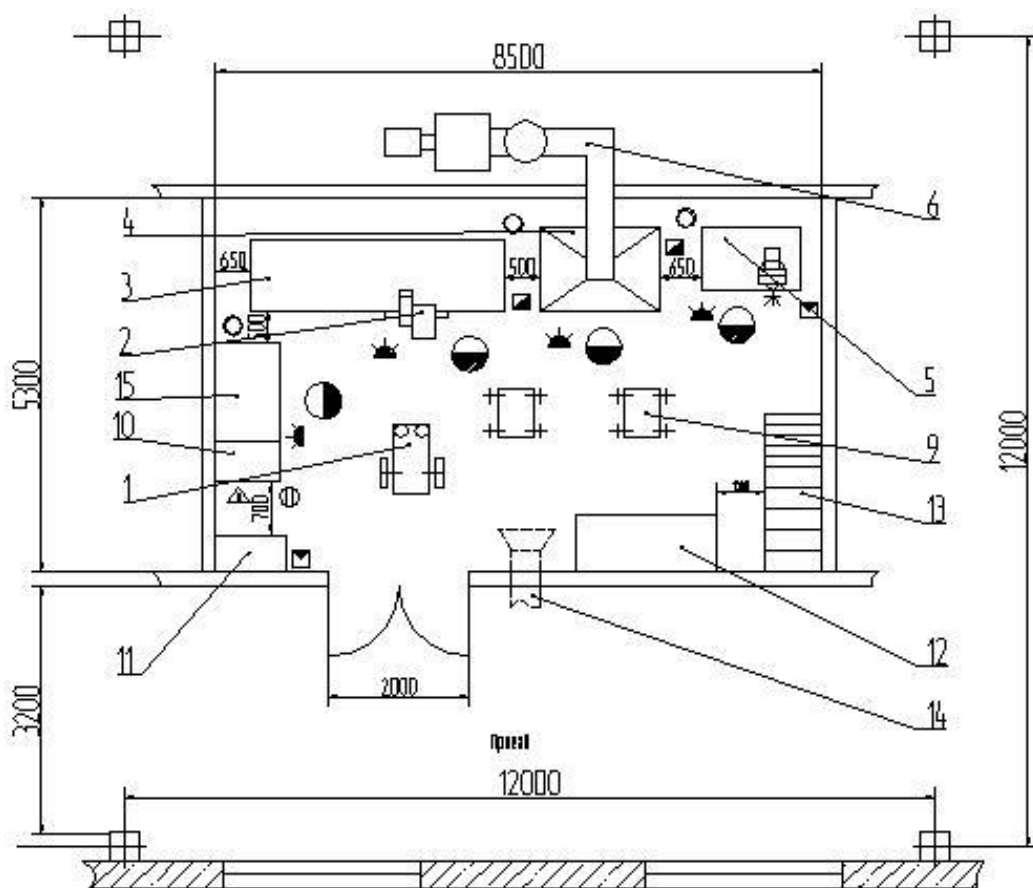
схема компоновочная участка сварки
